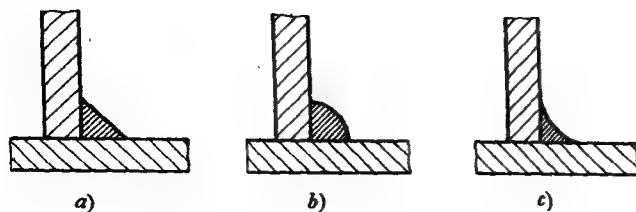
Clasificación de las soldaduras según la forma de la superficie exterior: a) plana; b) reforzada; c) aligerada (*).
